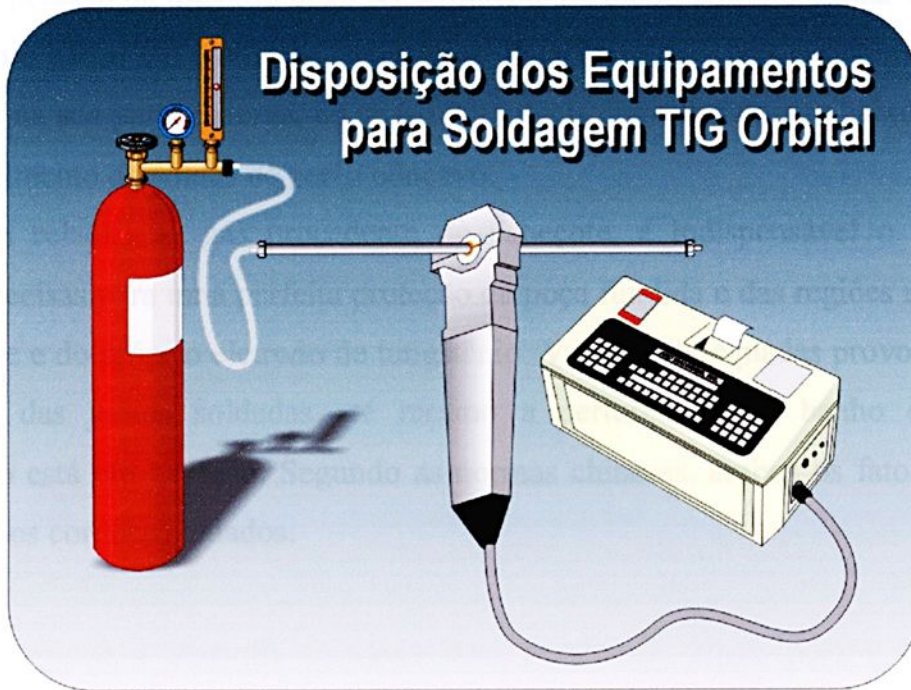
Arranjo dos equipamentos para a execução da soldagem TIG orbital
